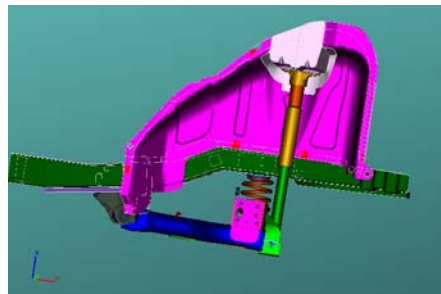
Montagem de suspensão, caixa de roda e Top Mount (cortesia da Ford Motor Company© do Brasil Ltda)
